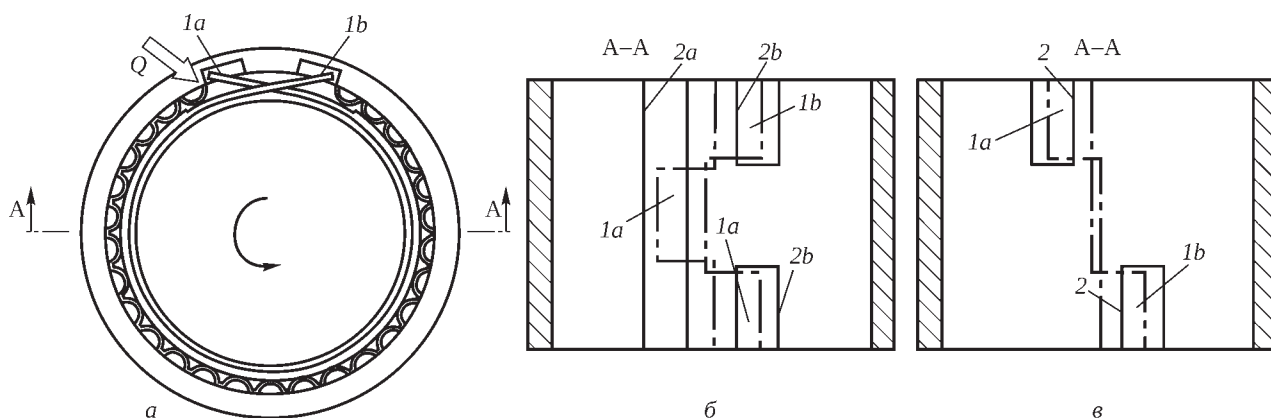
Схема подшипника с гладким лепестком без жесткого крепления к обойме [26]:
